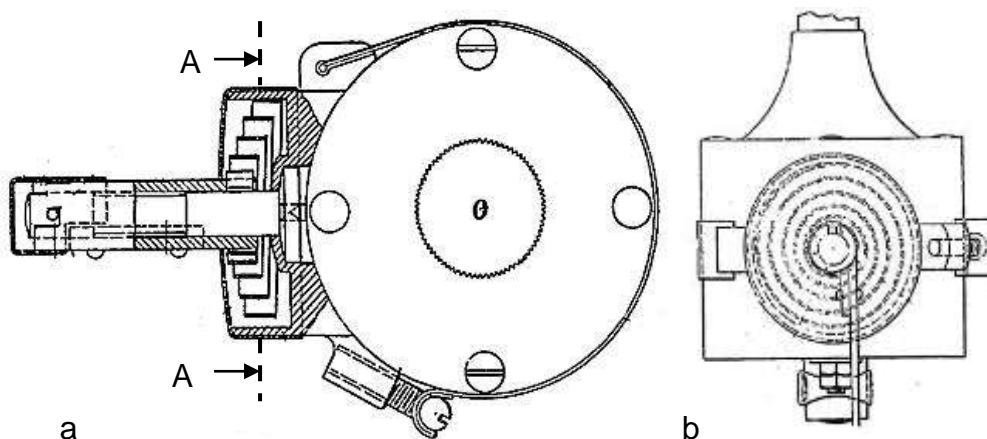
Zeichnungen im Patent Nr. 333954: a) Drehbolzen mit Spiralfeder, b) Schnitt A-A
